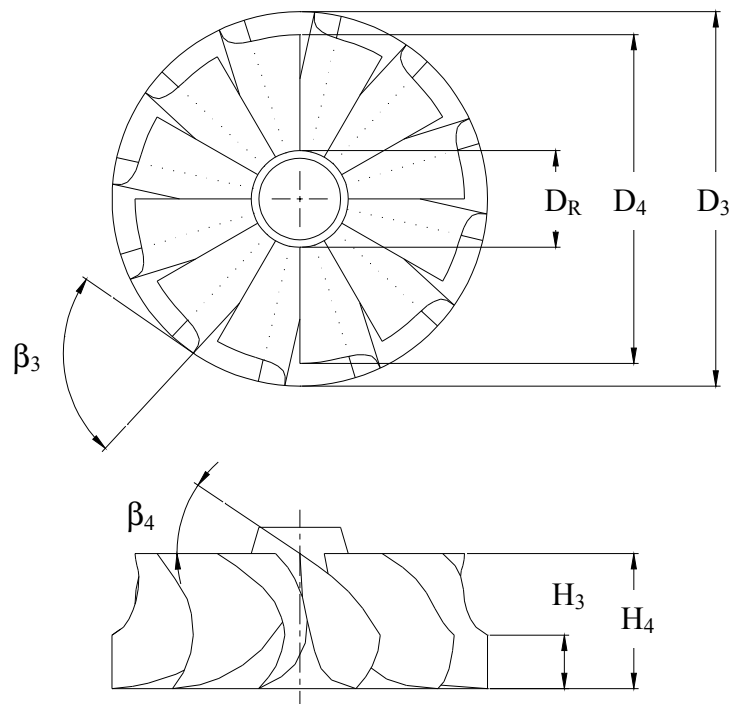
Dimensões Características do Rotor da Turbina
